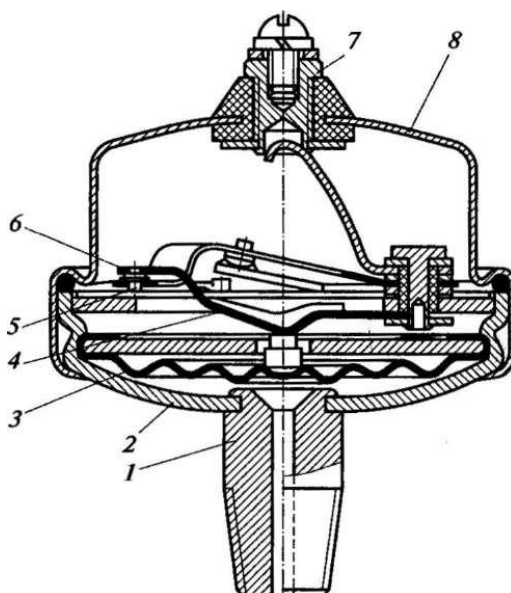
Мембранный датчик аварийного давления масла: 1 — штуцер; 2 — корпус; 3 — мембрана; 4 — рычаг выключателя; 5 — неподвижный контакт; 6 — подвижный контакт; 7 — выводной контакт; 8 — кожух
